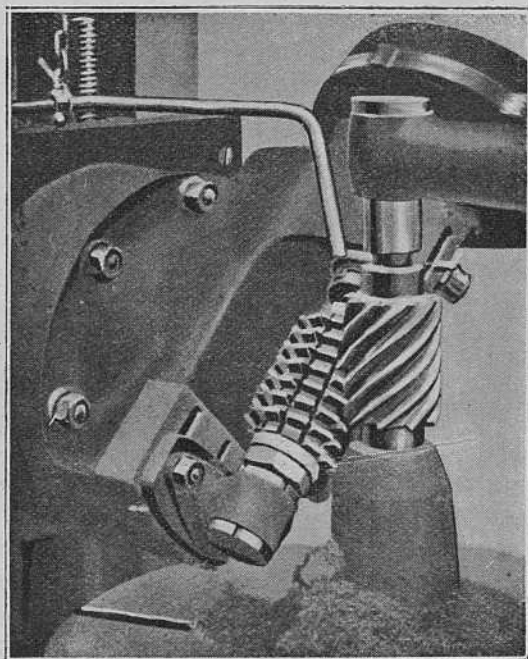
Máquina Renania cortando engranajes helicoidales
